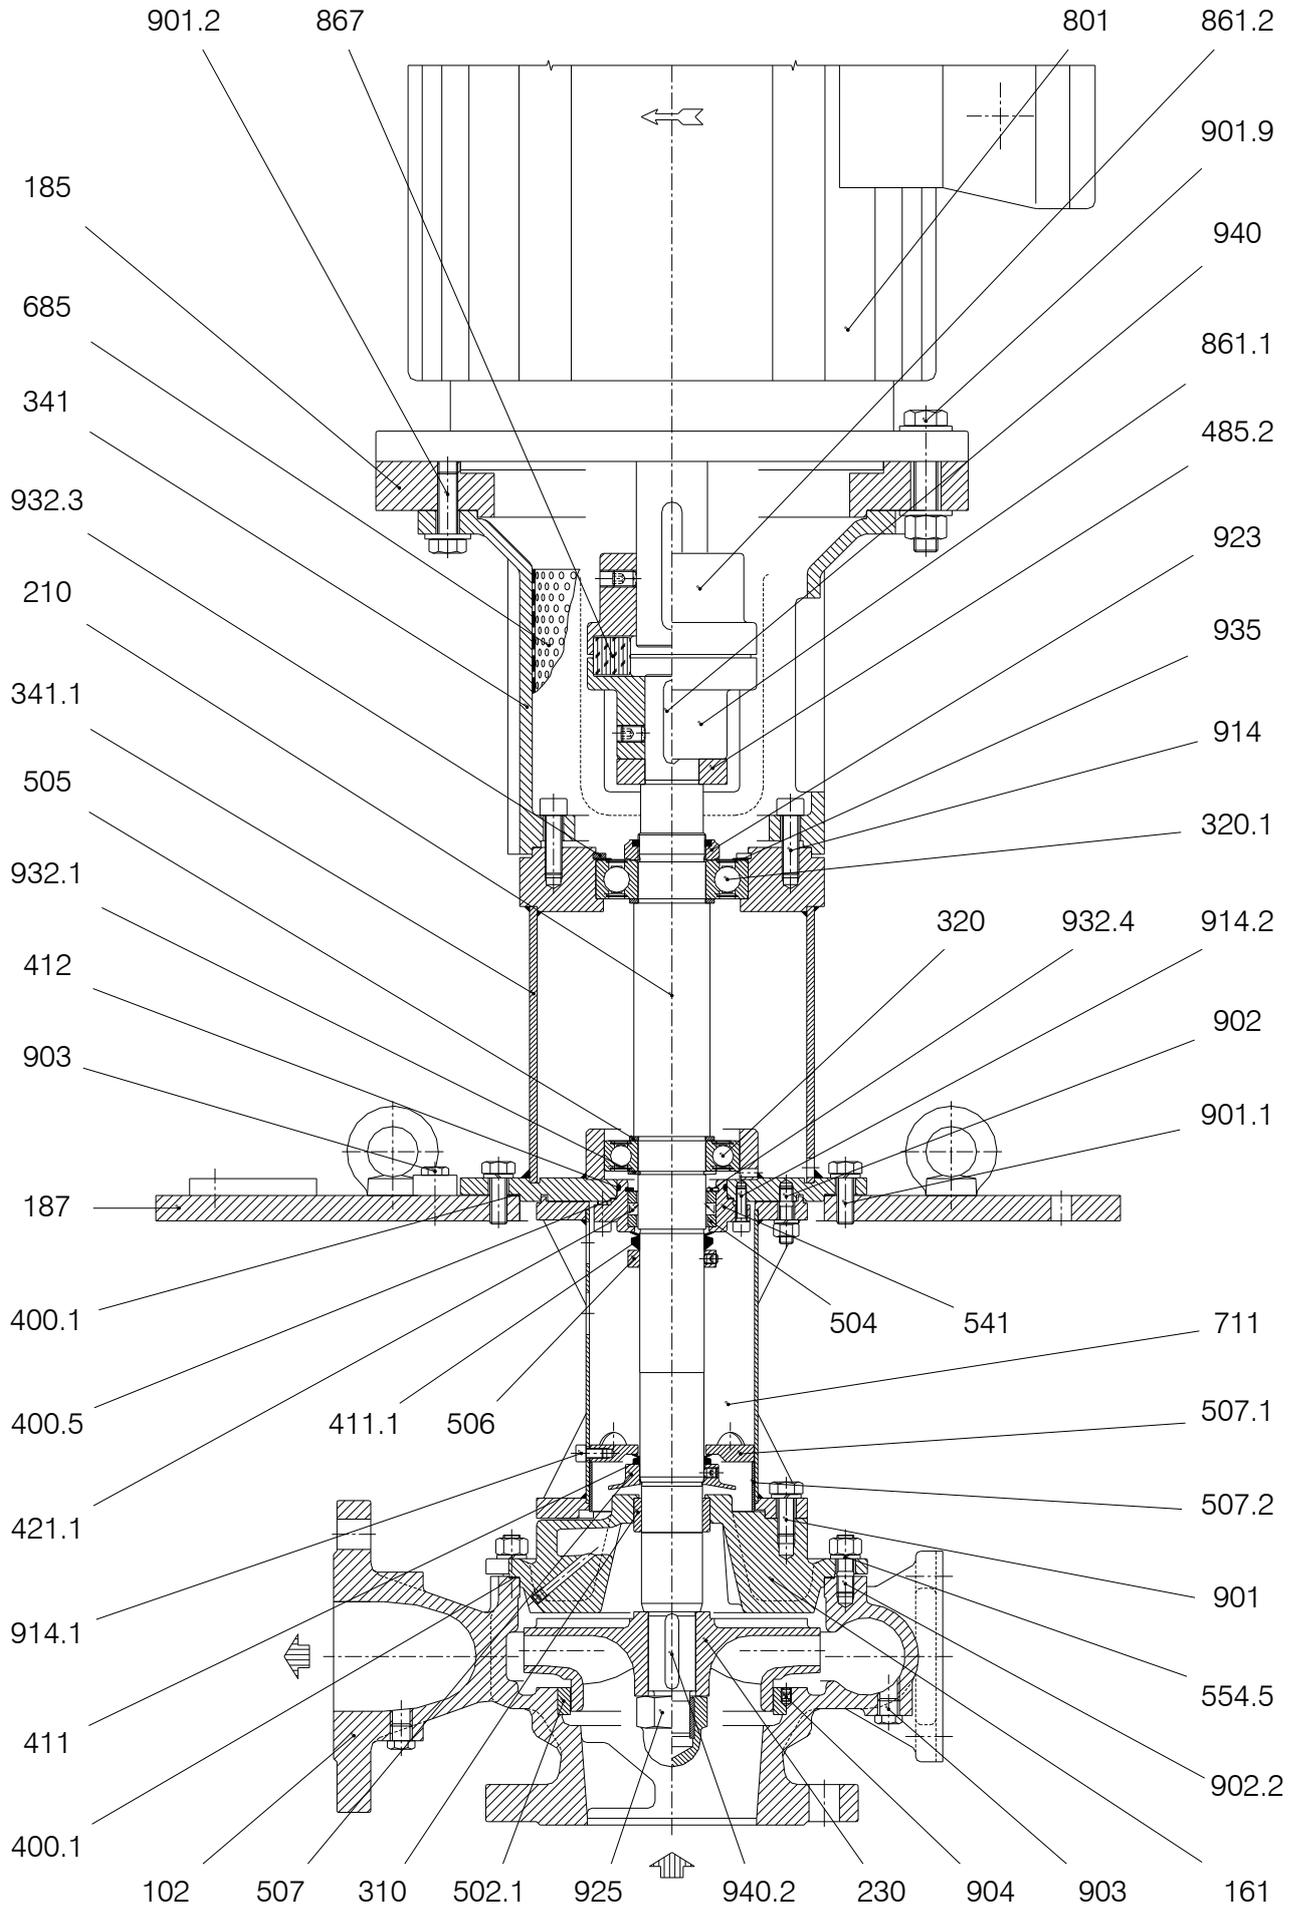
Pumpenserie TCHV in Ausführung /1-L1 = Dichtungsbuchse mit Radialdichtring
